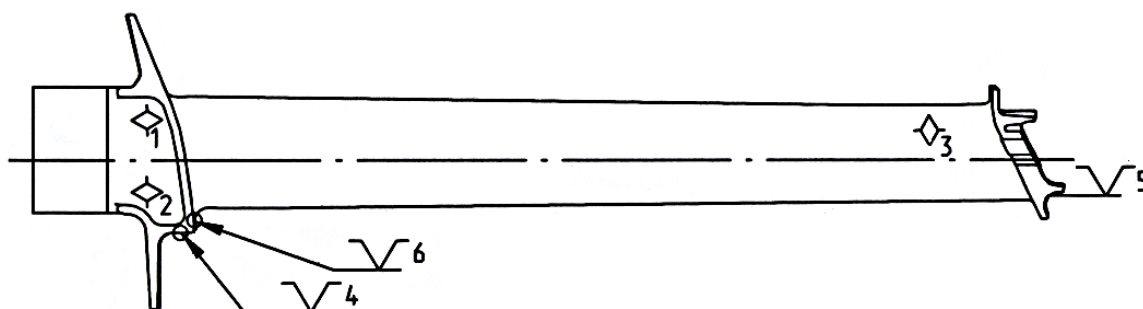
Базовые поверхности литой заготовки турбинной лопатки
